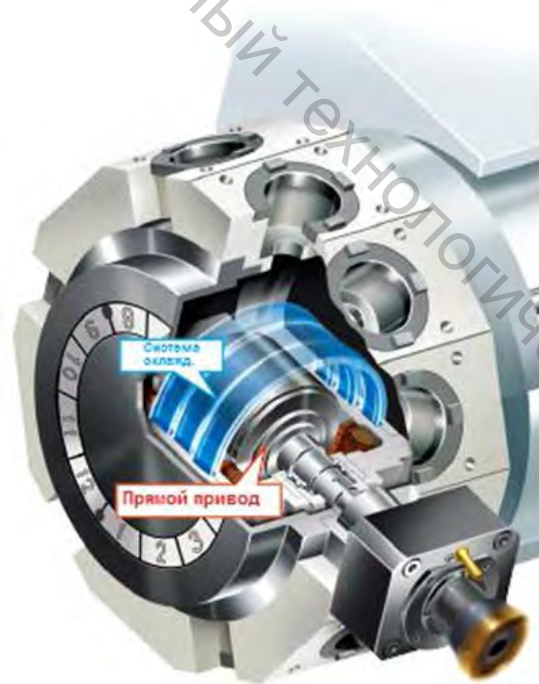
Конструктивное исполнение револьверной головки с прямым приводом для токарно-фрезерного станка с ЧПУ
